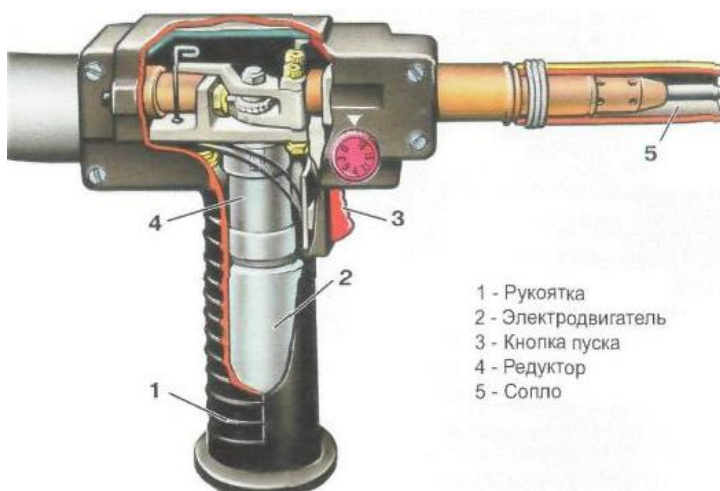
Горелка с механизмом подачи проволоки тянущего типа
